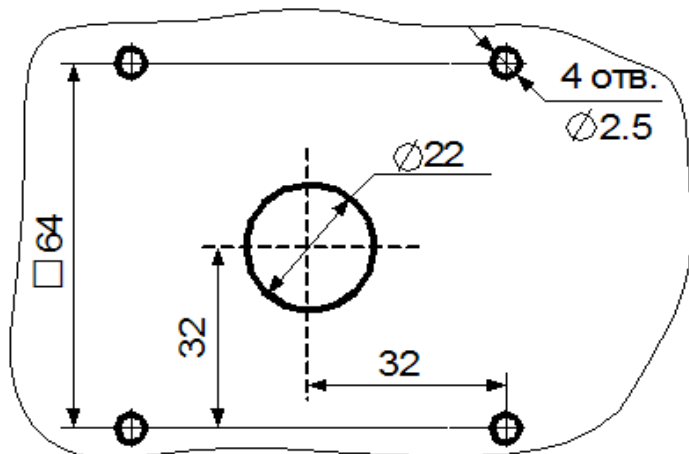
Чертеж разметки на баке для сверления отверстий для установки датчика.
